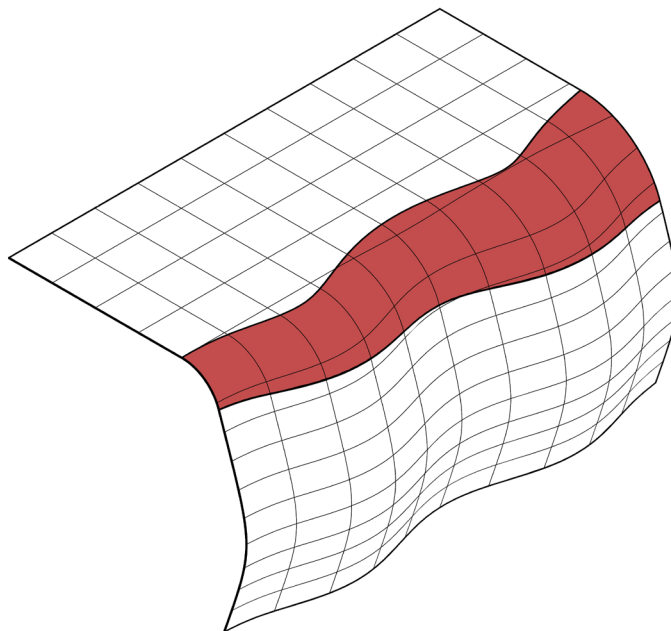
Resultado *Fillet Chamfer Edge 1*.
